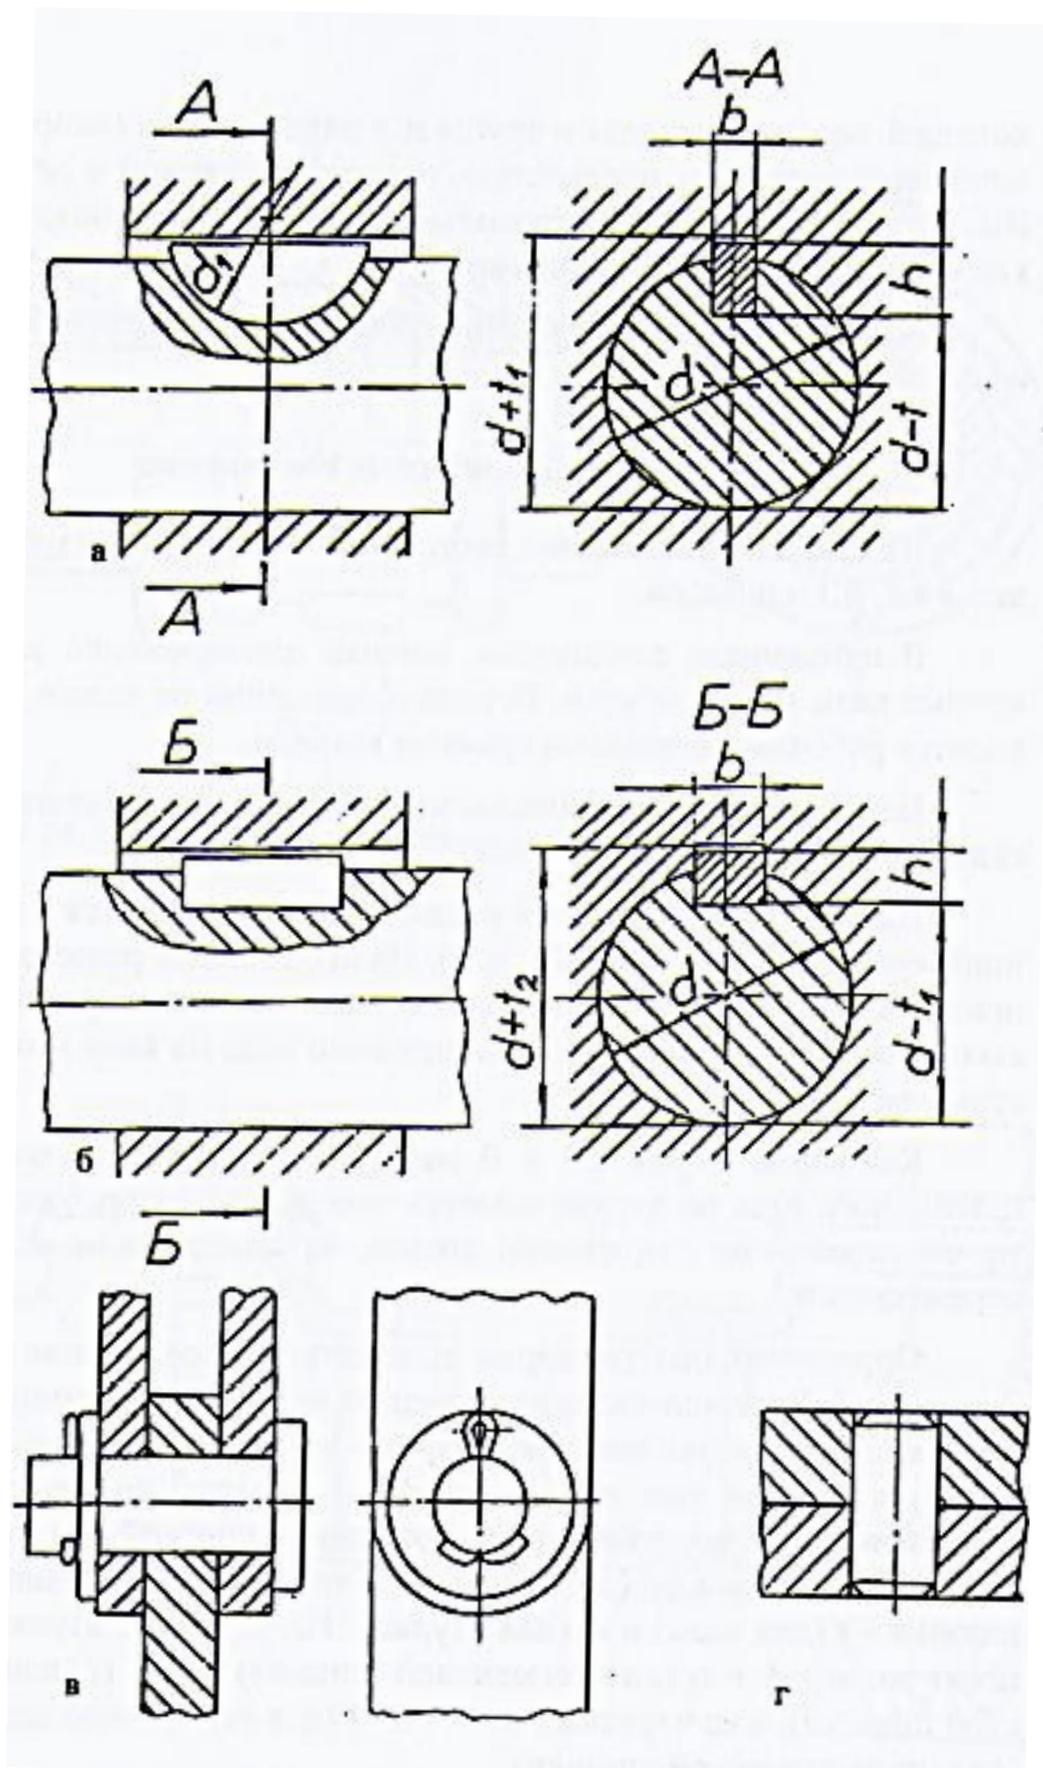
Неподвижные соединения: а – шпоночное (сегментная шпонка); б – шпоночное (призматическая шпонка); в – шплинтовое; г – штифтовое
